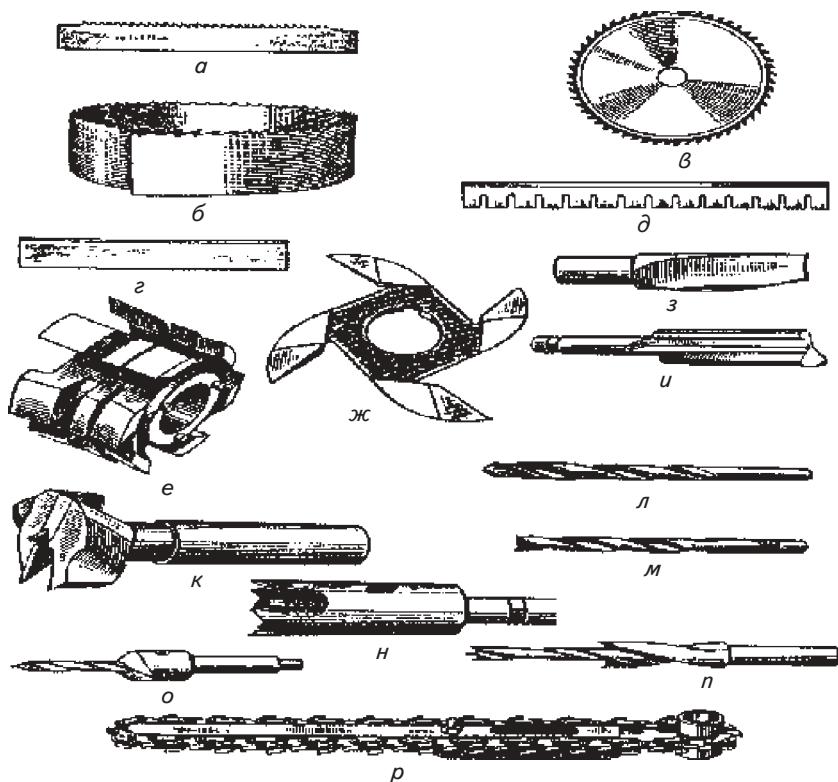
Станочный дереворежущий инструмент общего назначения:
